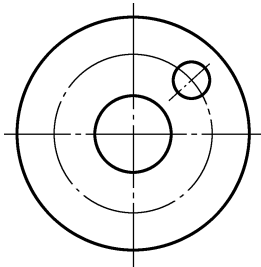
滚动轴承在垂直于轴线投影面的特征画法
